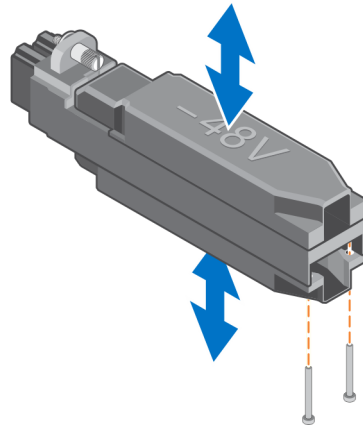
Entfernen der zwei 1,5-mm-Sechskantschrauben und Trennen des Gehäuses
